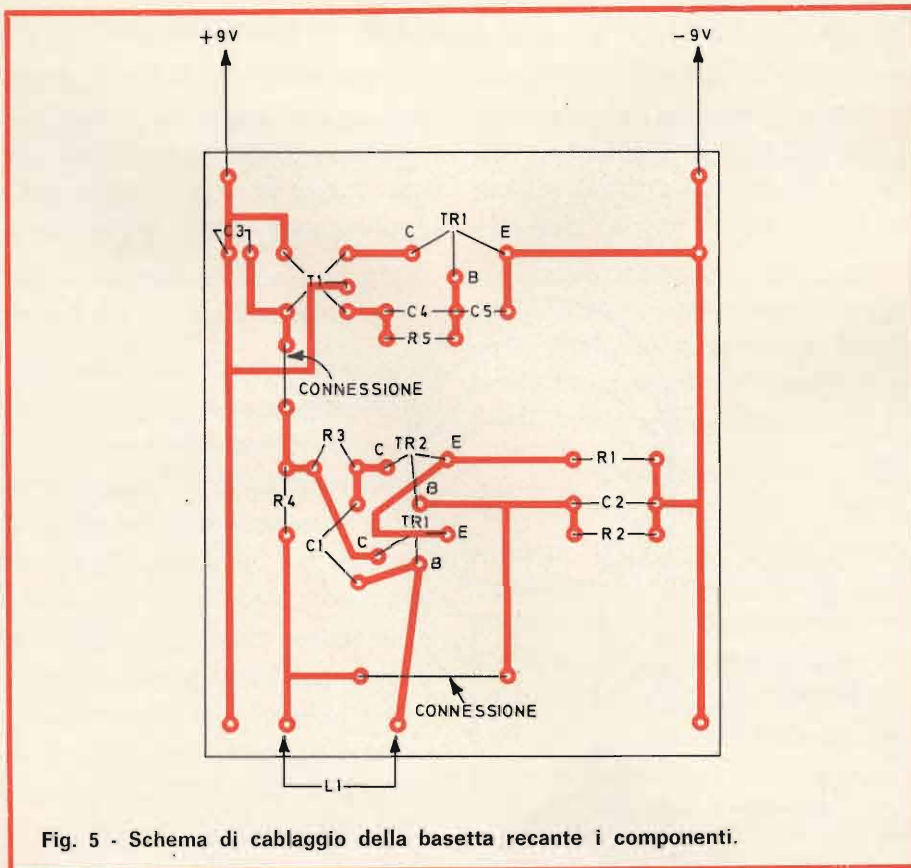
Schema di cablaggio della basetta recante i componenti.
